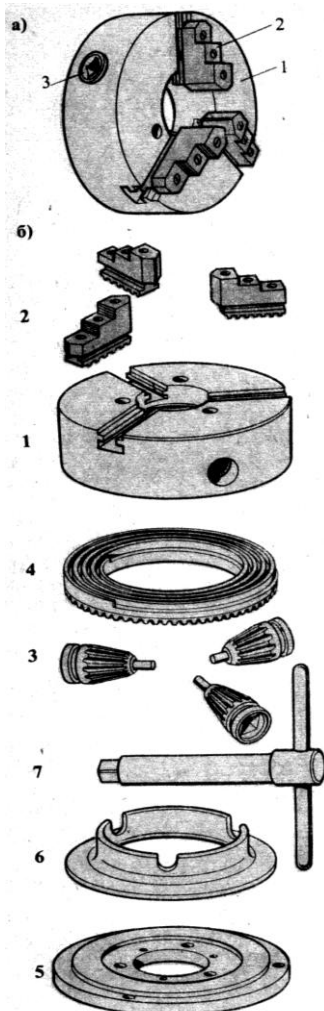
Трьохкулачковий самоцентрувальний патрон:
